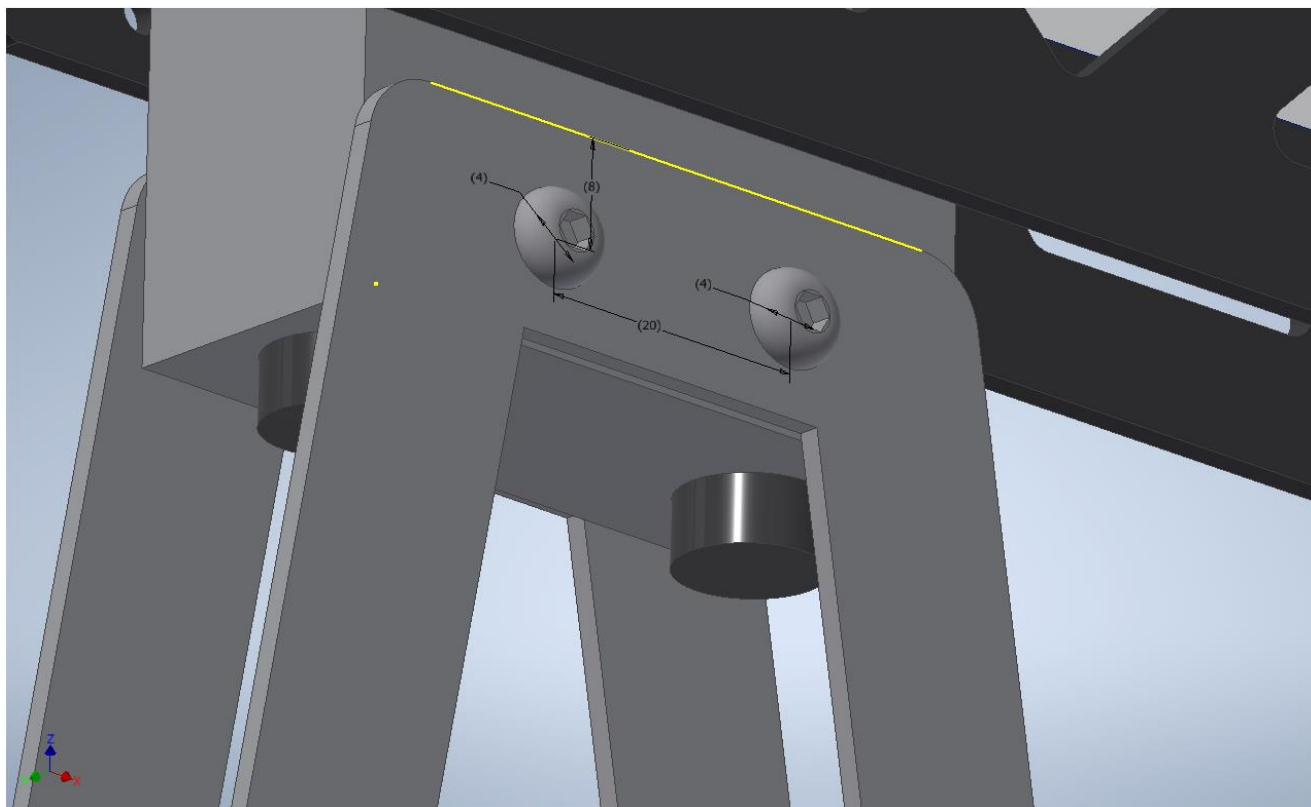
Схема закрепления пластин к рейке крепления полезной нагрузки.
